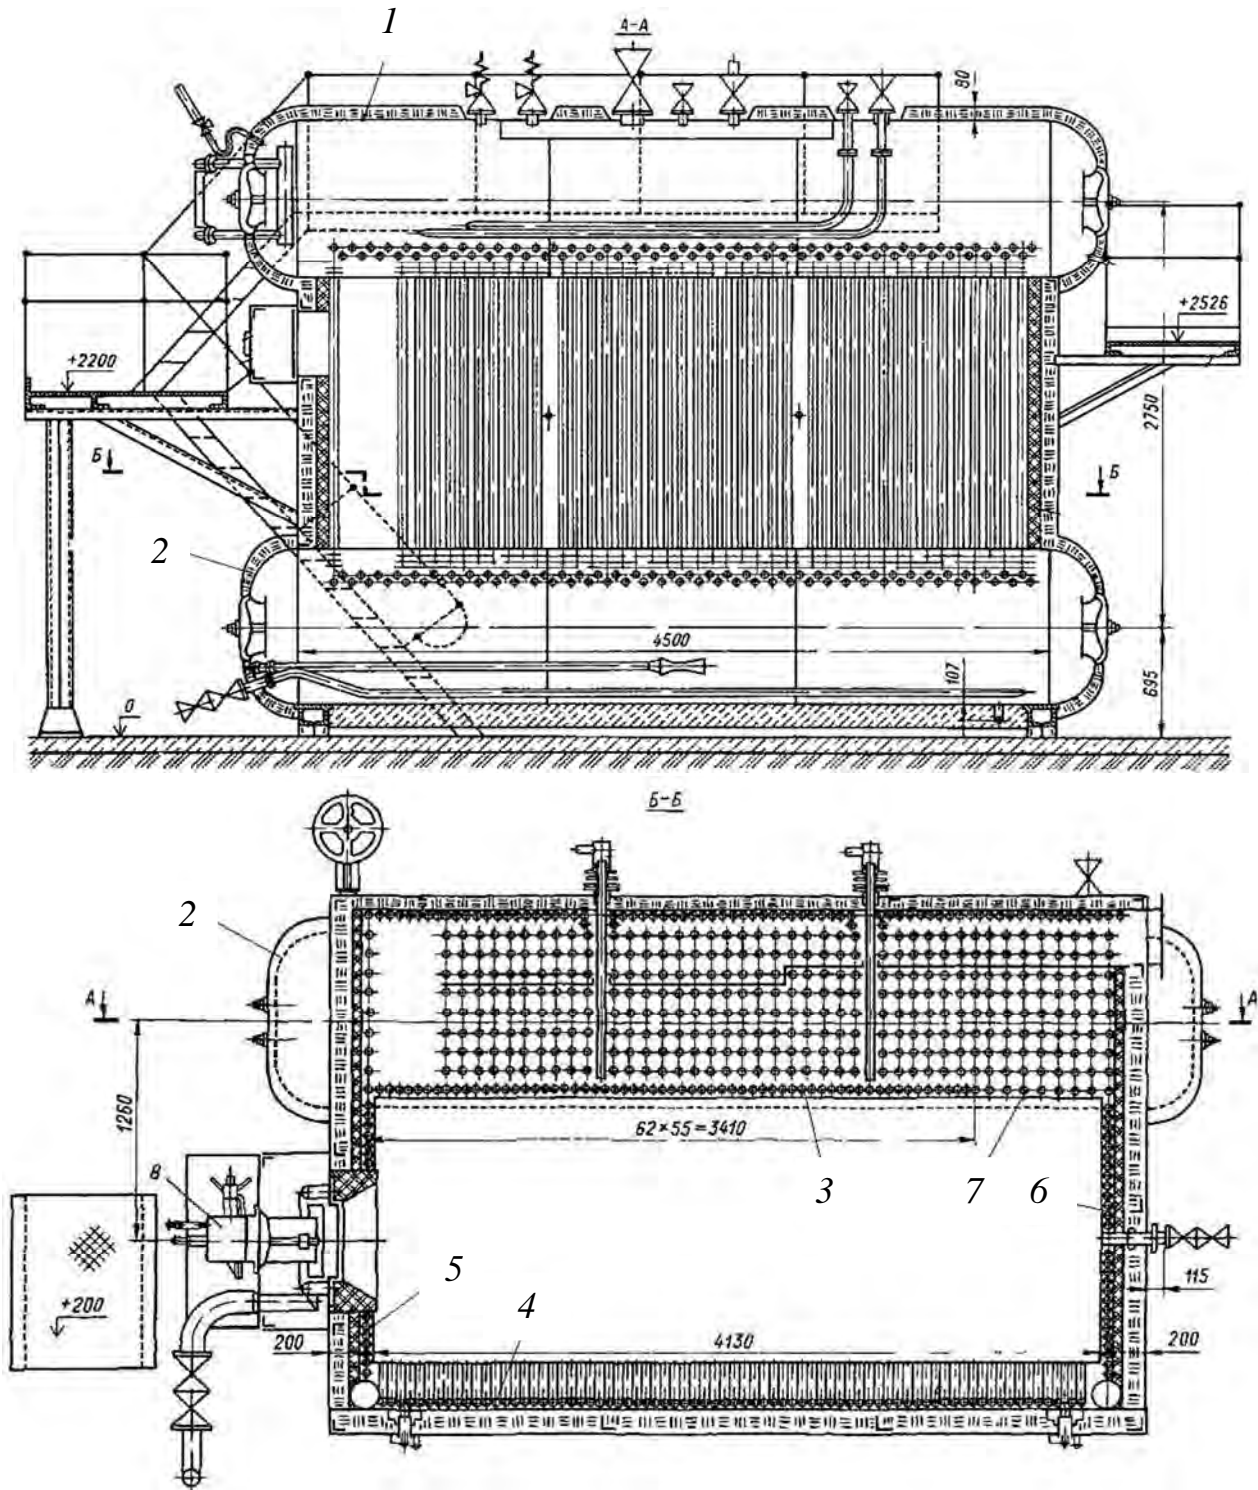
Котел ДЕ-10/14: 1 – верхний барабан; 2 – нижний барабан; 3 – газоплотный (левый) боковой экран; 4 – правый боковой экран; 5 – фронтальный экран; 6 – задний экран; 7 – конвективный пучок
